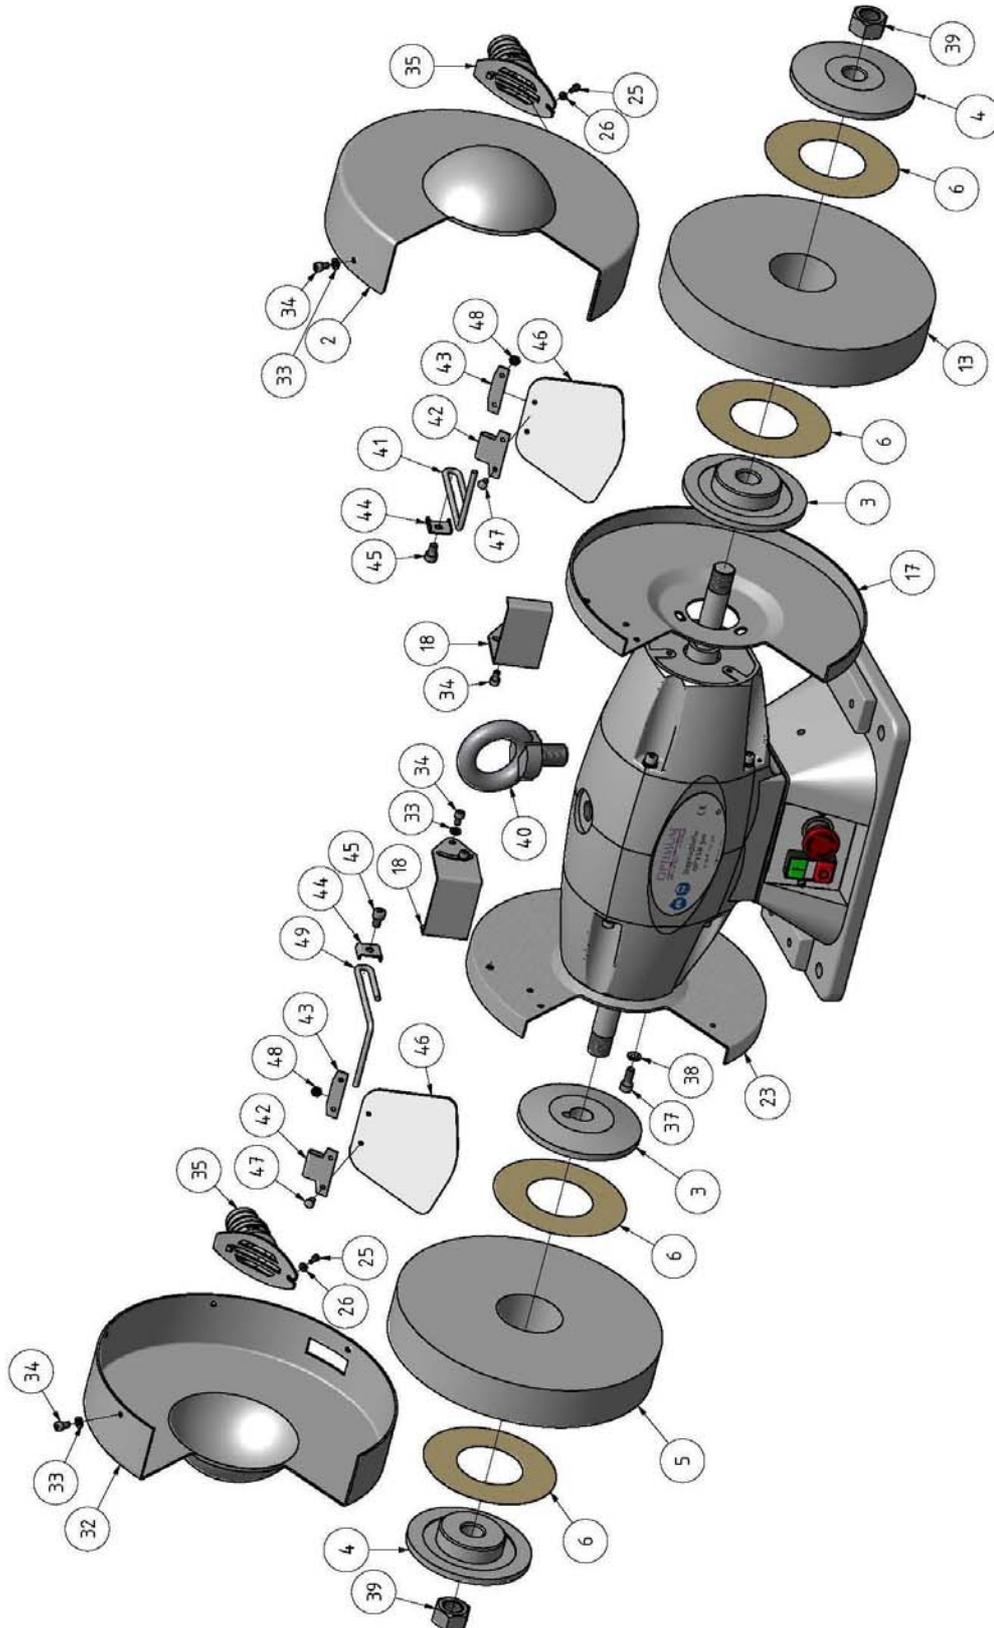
Ersatzteilzeichnung 1 von 2 - Drawing spare parts 1 of 2
